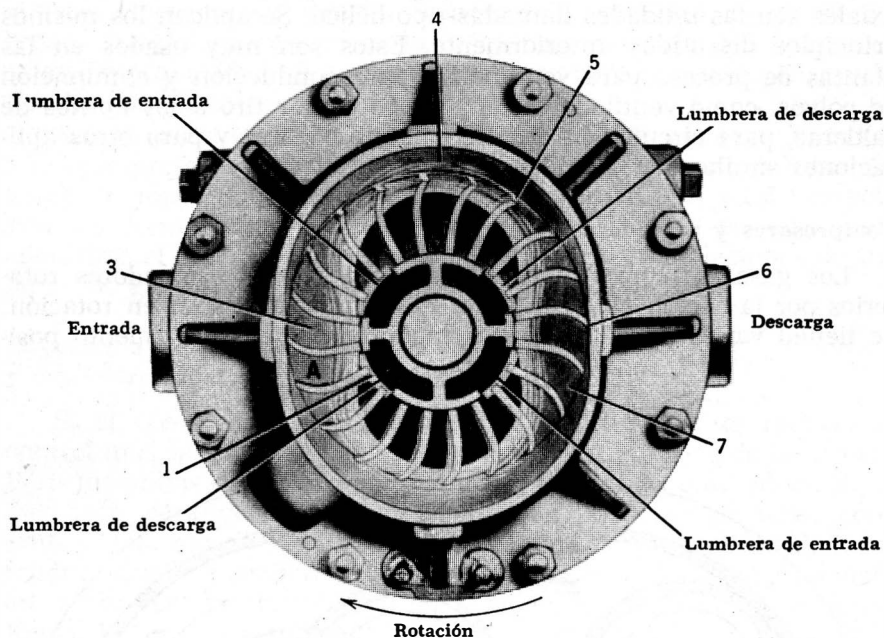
Compresor de pistón líquido rotatorio. (Cortesía de Nash Engineering Company.)
